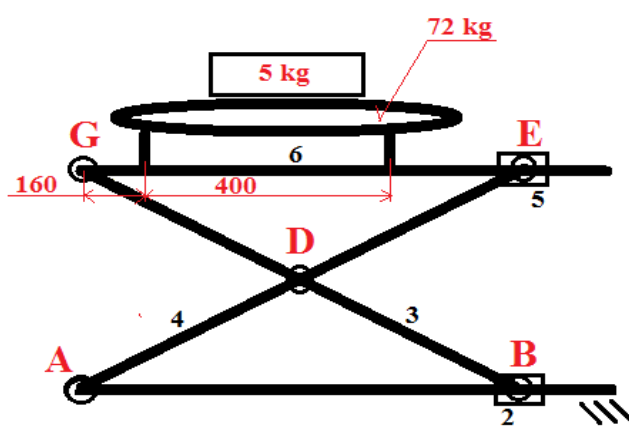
Zvedák s lineárním pojezdem řešeným kladkami Rolle 39
